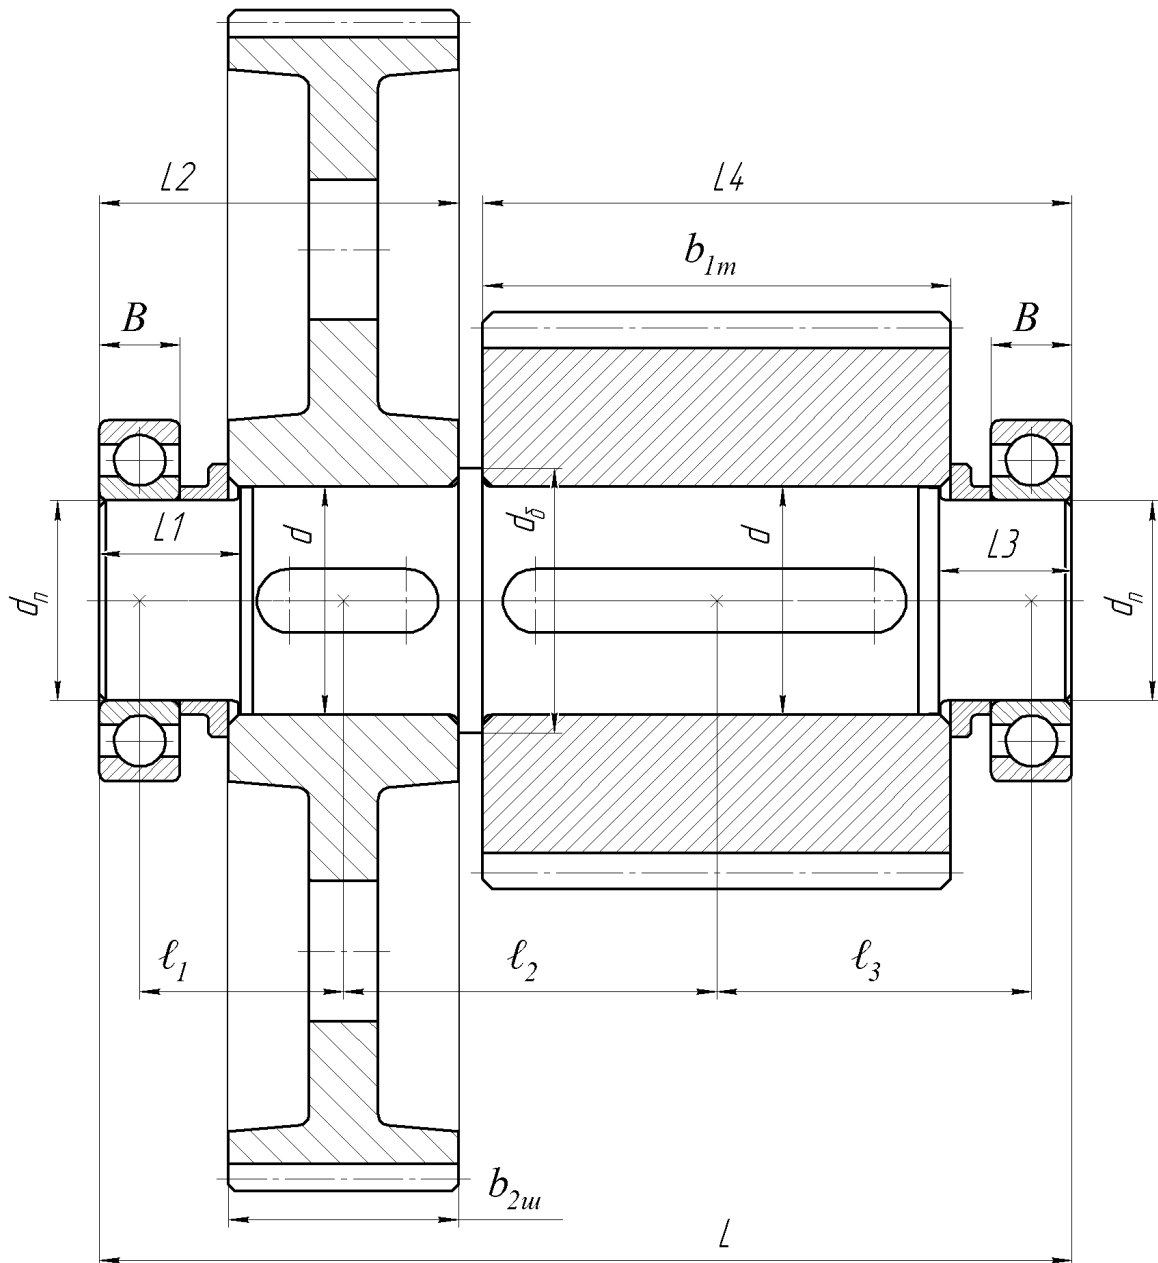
Розрахункова схема проміжного вала редуктора
